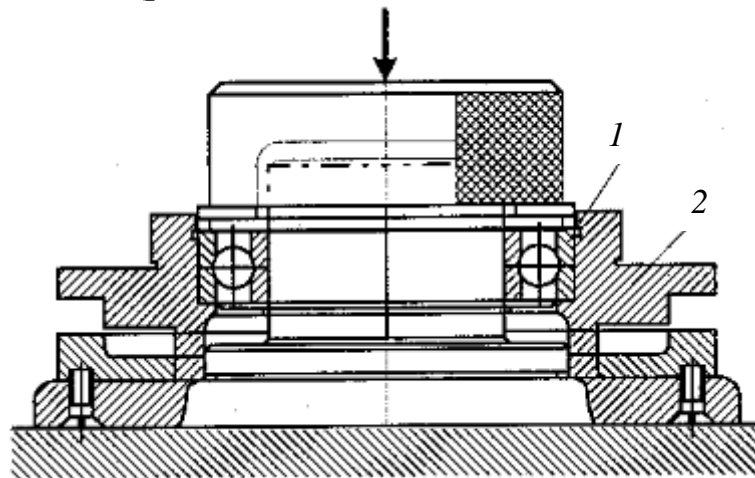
Базирование в приспособлении подшипника 1 и корпуса 2 при сборке узла
